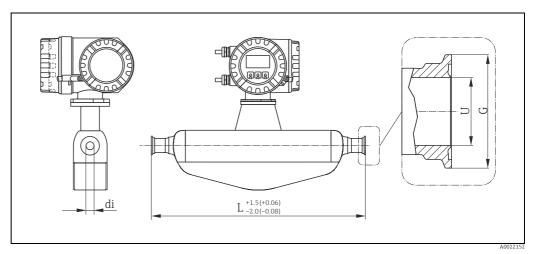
Detail A: Der Flansch hat auf der Messaufnehmerseite die kleinere Nut für den O-Ring. Bei der Montage muss der Rohrflansch über die entsprechend größere Nut verfügen. Maßeinheit (mm) in.
